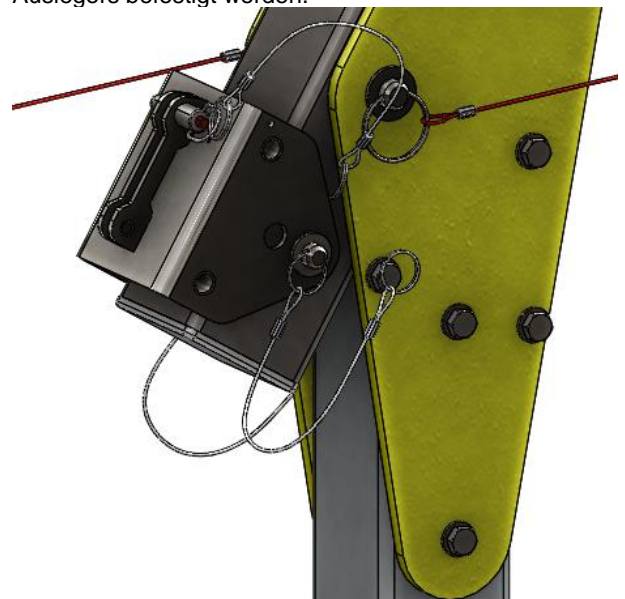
am Ende des Auslegers befestigte Universal-Windenhalterung PAD100-301-000
